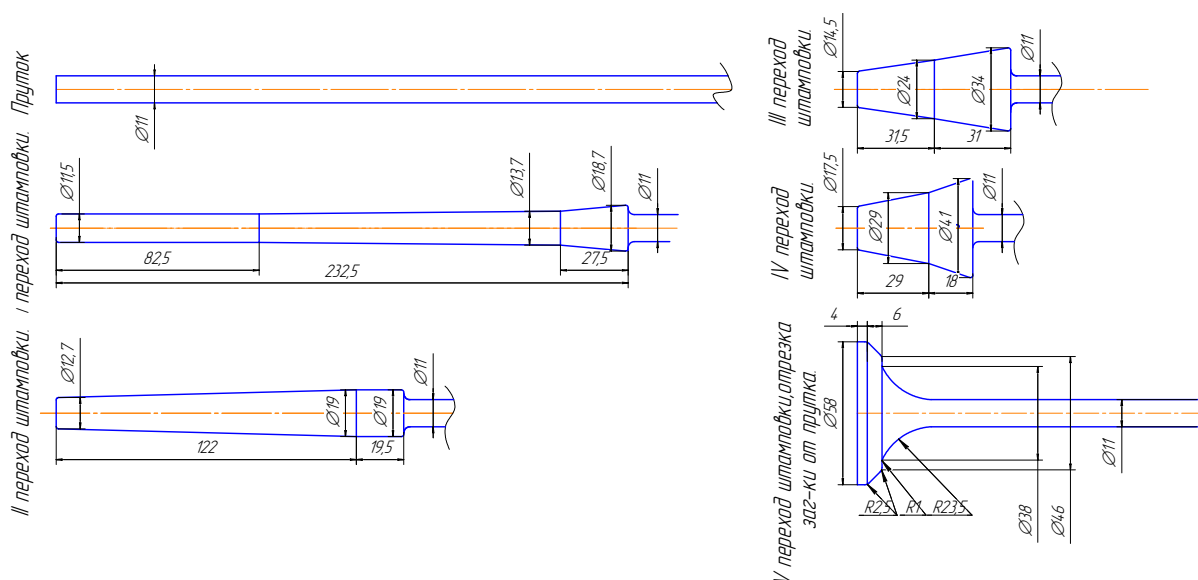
Штамповка заготовки на ГКМ за пять переходов, с последующей отрезкой заготовки от прутка
